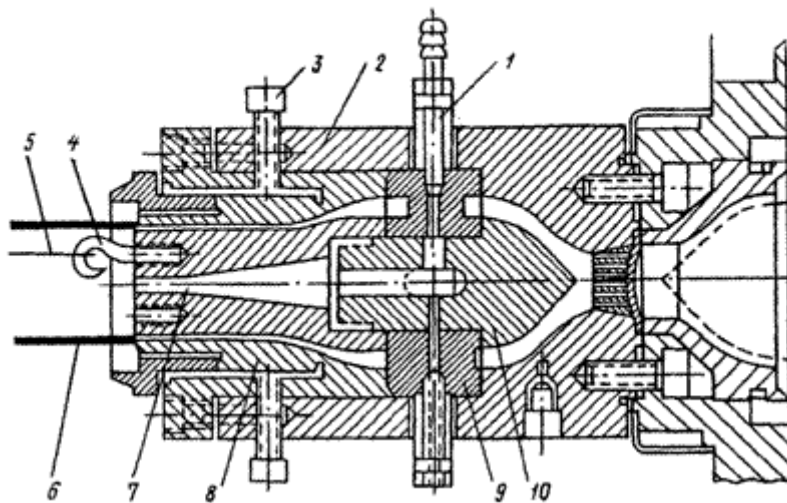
Прямоточная кольцевая головка для изготовления труб и шлангов:
